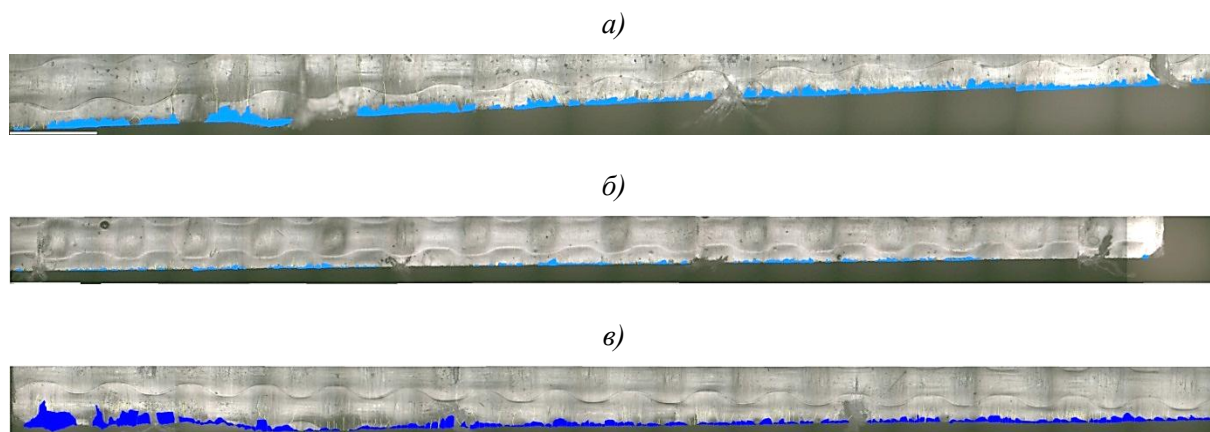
Панорамный снимок ($\times 100$) торцевой поверхности плиты из углепластика, обработанной с помощью роботизированного фрезерного станка (*а*), а также абразивным (*б*) и алмазным кругами (*в*), с резом в продольном (*а*) и поперечном (*б*, *в*) направлениях относительно волокон наполнителя
